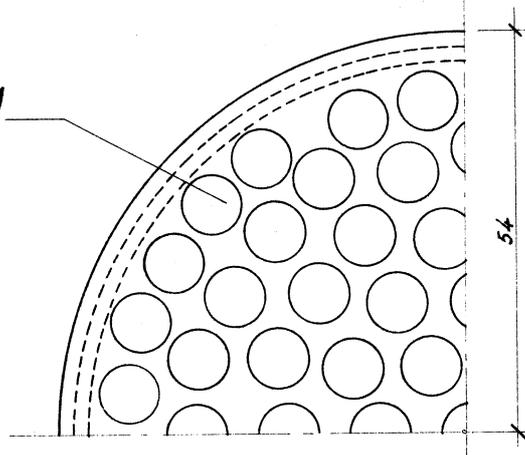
PONTA PARA PIEZÔMETRO ABERTO
